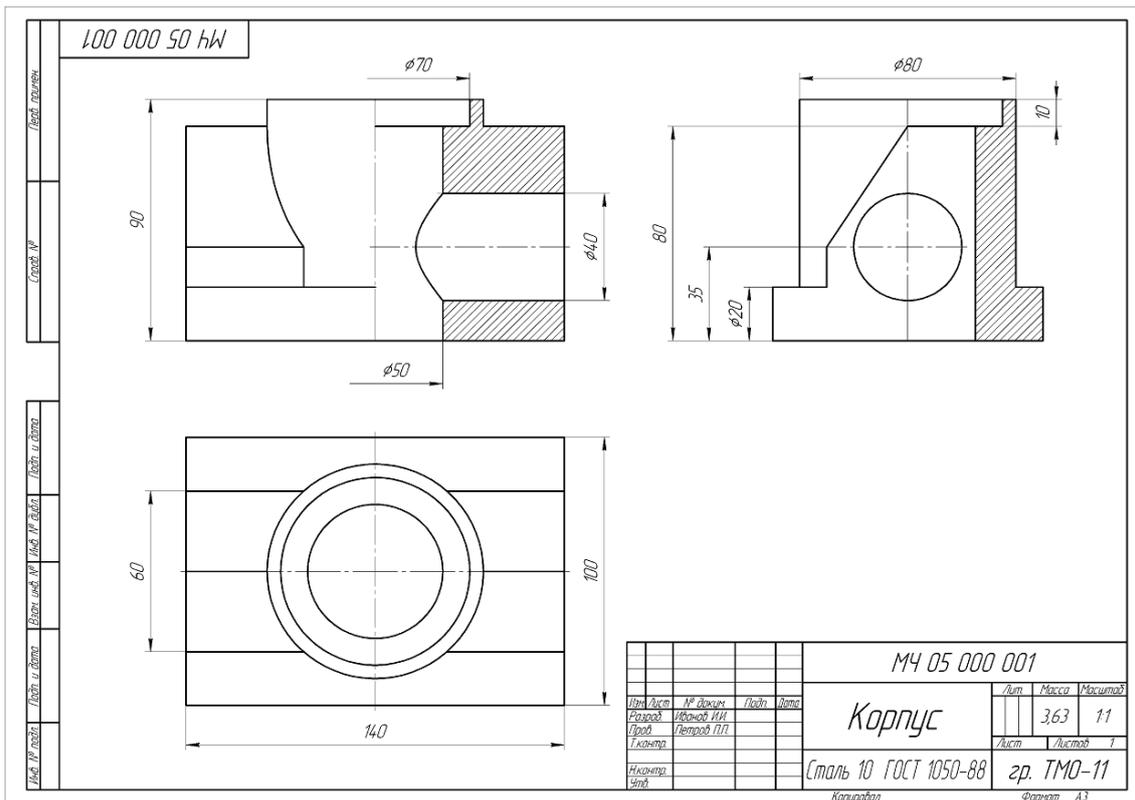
Пример выполнения чертежа детали «Корпус» при совмещении главного вида с разрезом
